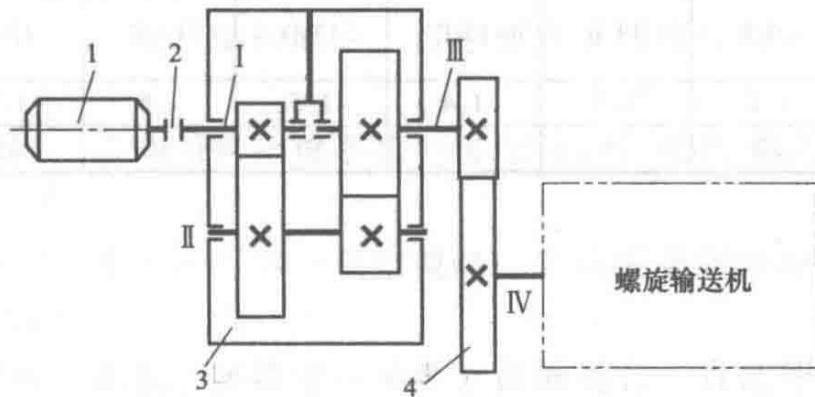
二级同轴式圆柱齿轮减速器+开式齿轮传动
